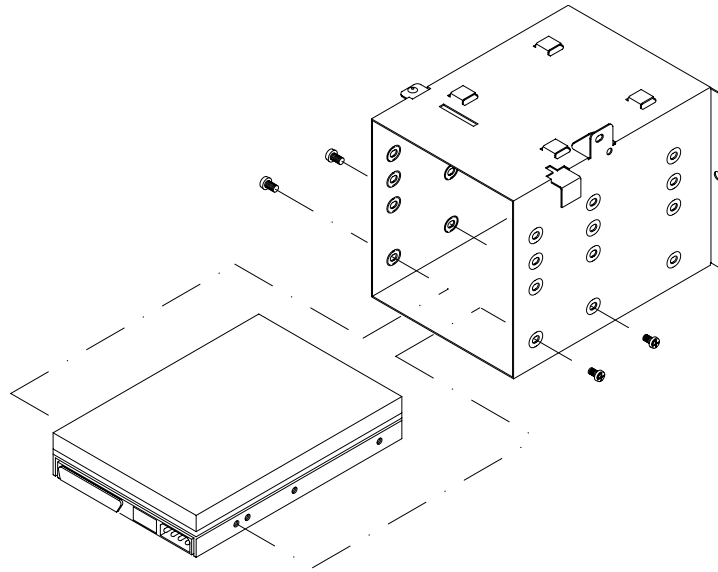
Démontage ou remplacement d'un dispositif à accès interne
